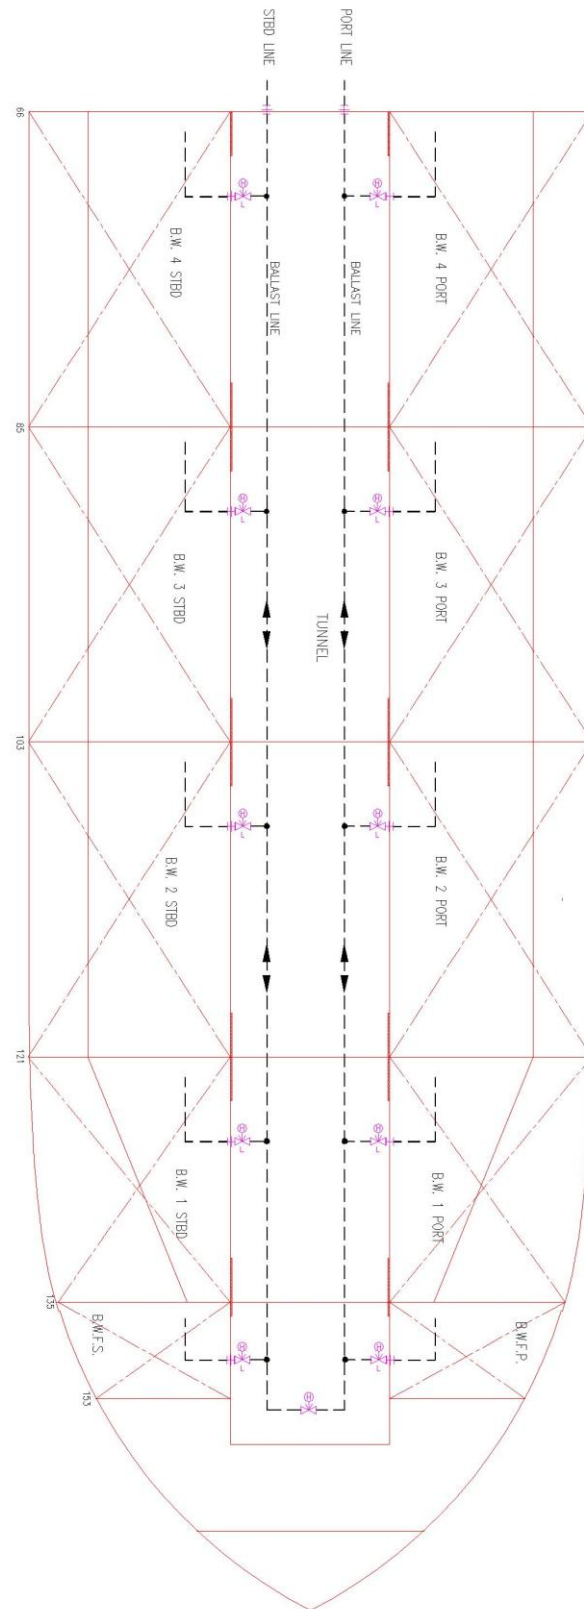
(Planta disposición lastre-zona de carga con túnel)
